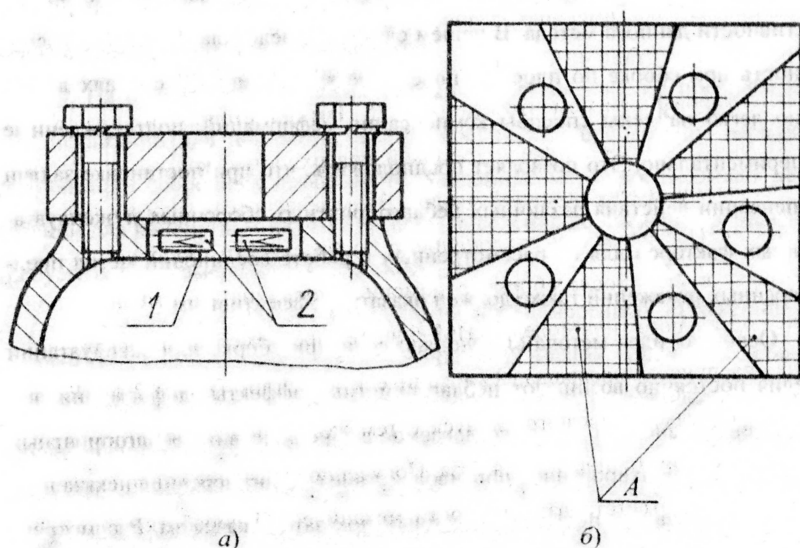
Схемы сборки и преднамеренных искажений пластины при сборке корпуса с ответной деталью
